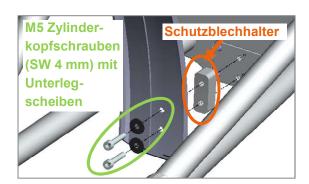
M5 Zylinderkopfschrauben zur Schutzblechbefestigung an Schutzblechhalter und Rahmen
